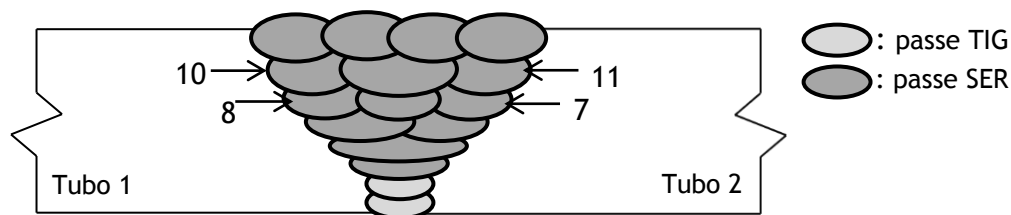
Sequência de passes da segunda soldadura.
